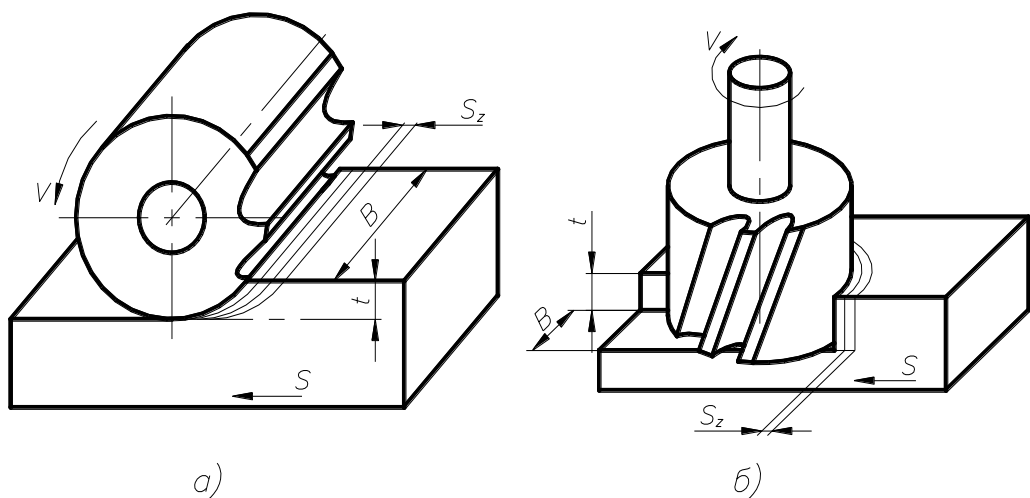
Виды фрезерования: а – цилиндрическое; б – торцевое.
